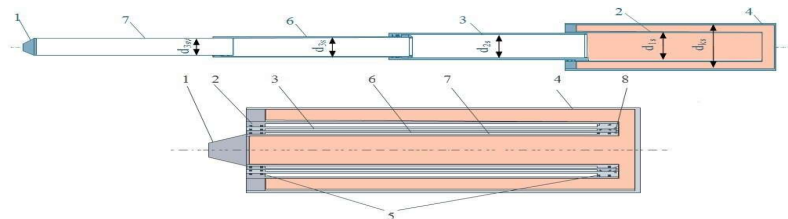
Схема трехступенчатого пневмоцилиндра с ресивером:
